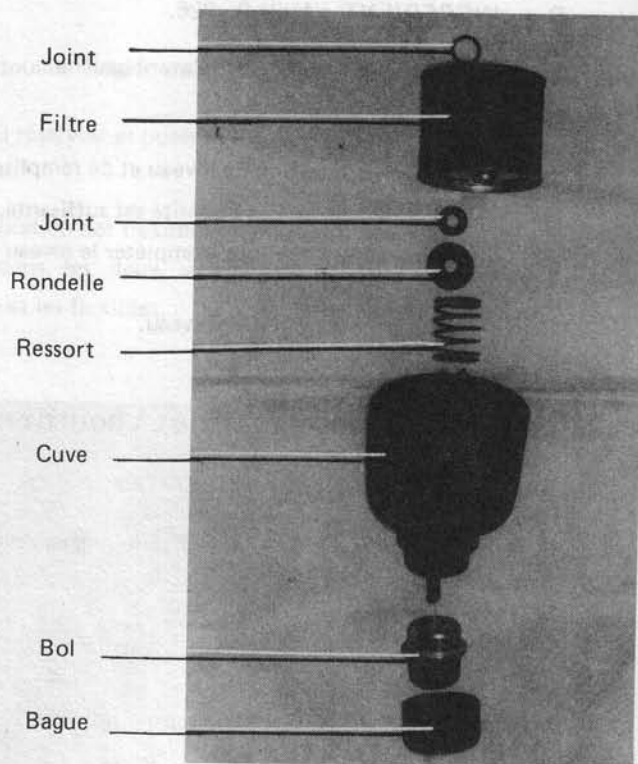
VUE ECLATEE DU PREFILTRE DE CARBURANT.
